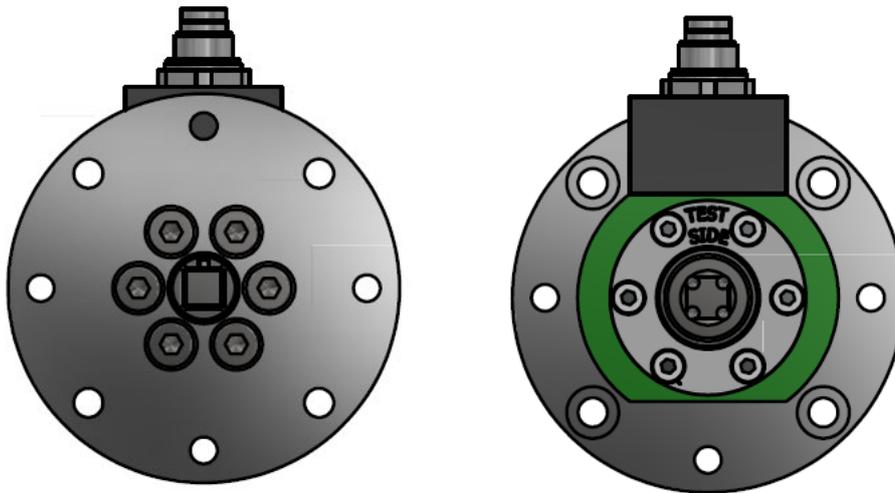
Montageflansch zur einfachen Befestigung – Sicht auf Befestigungs-/Messeite
